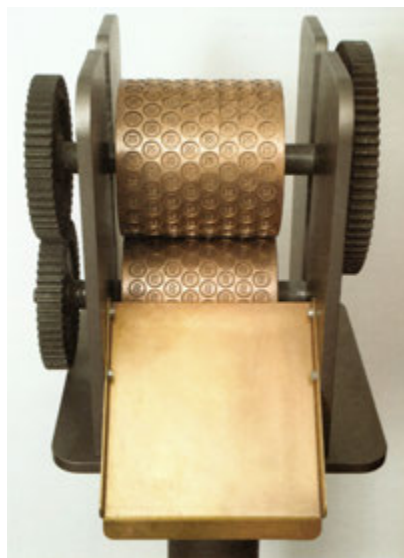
Stampatrice per caramelle, Baratti & Milano. Archivio Storico.
